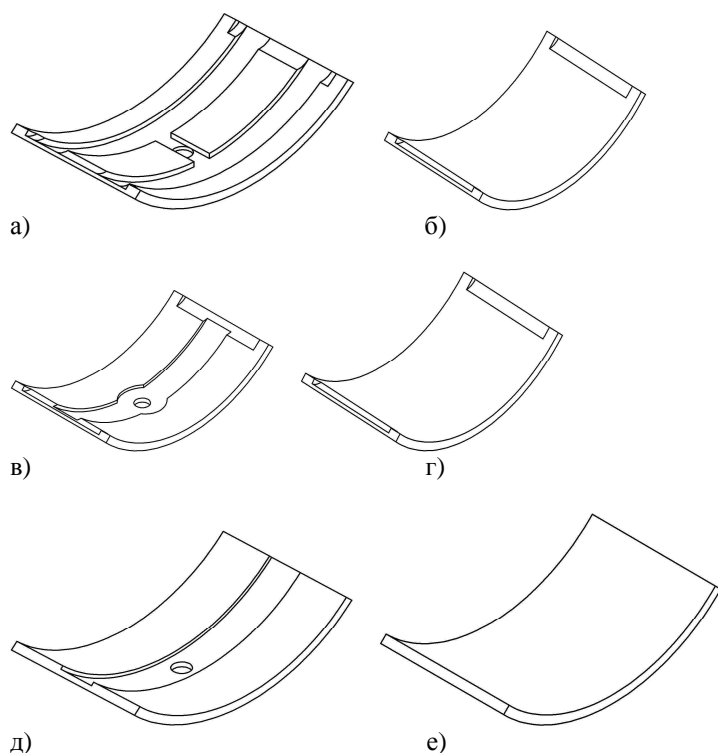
Конструкция вкладышей двигателя D-355С:
